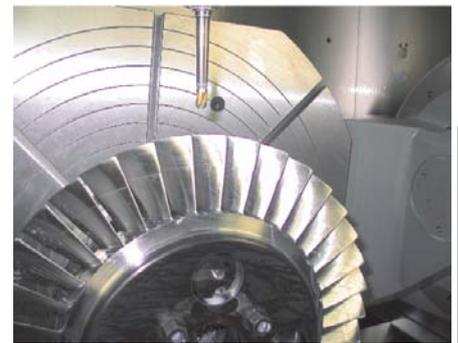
Обработка осевого моноколеса из титана концевой фрезой на ОЦ HERMLE C800U
